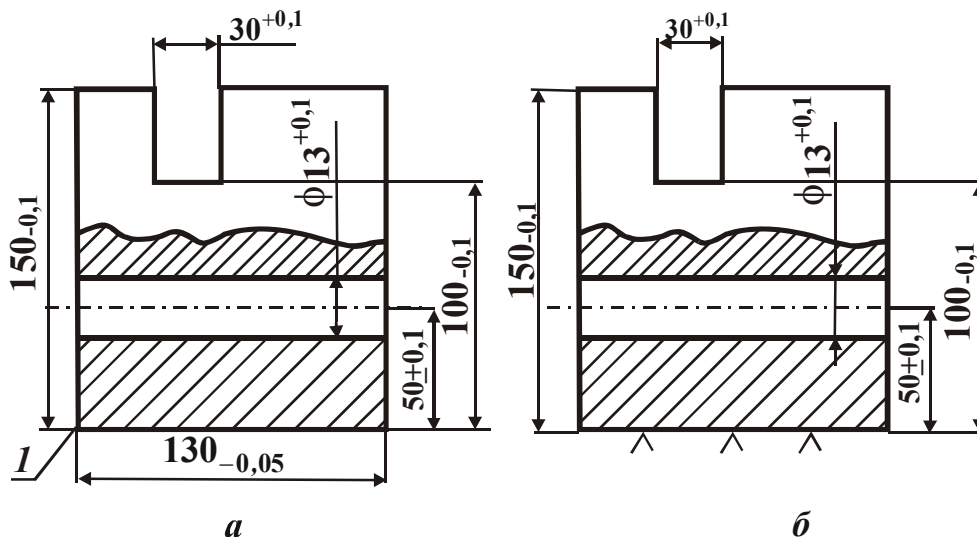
Чертеж детали (а) и операционный эскиз на обработку паза и сверления отверстия (б).
